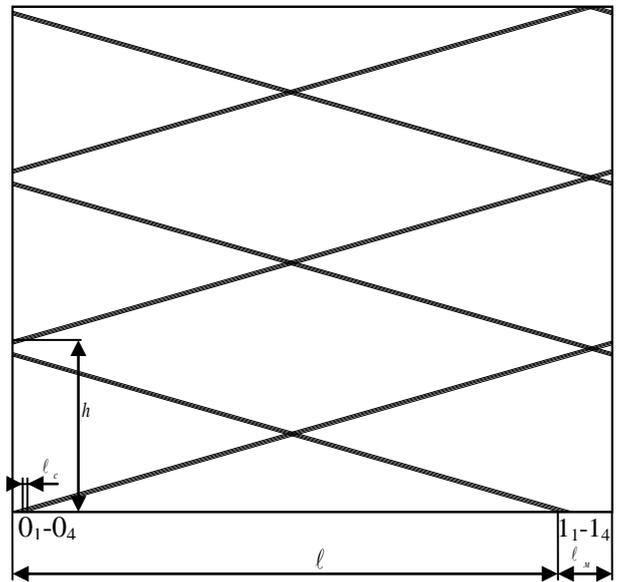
Развертка поверхности паковки бобинажно-мотальной машины БП-260-НШО
